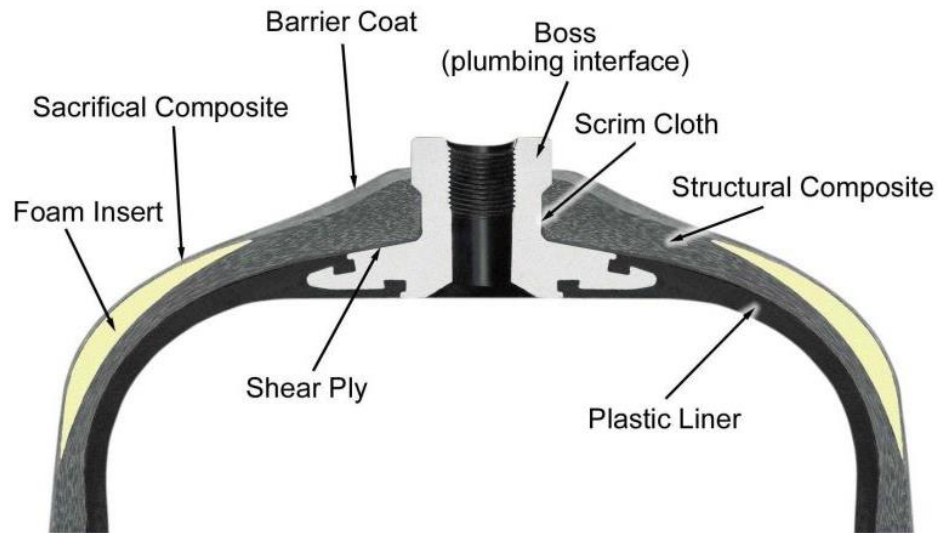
Конструкція паливного бака з неметалевим лейнером і заформованими металевими фланцями.
